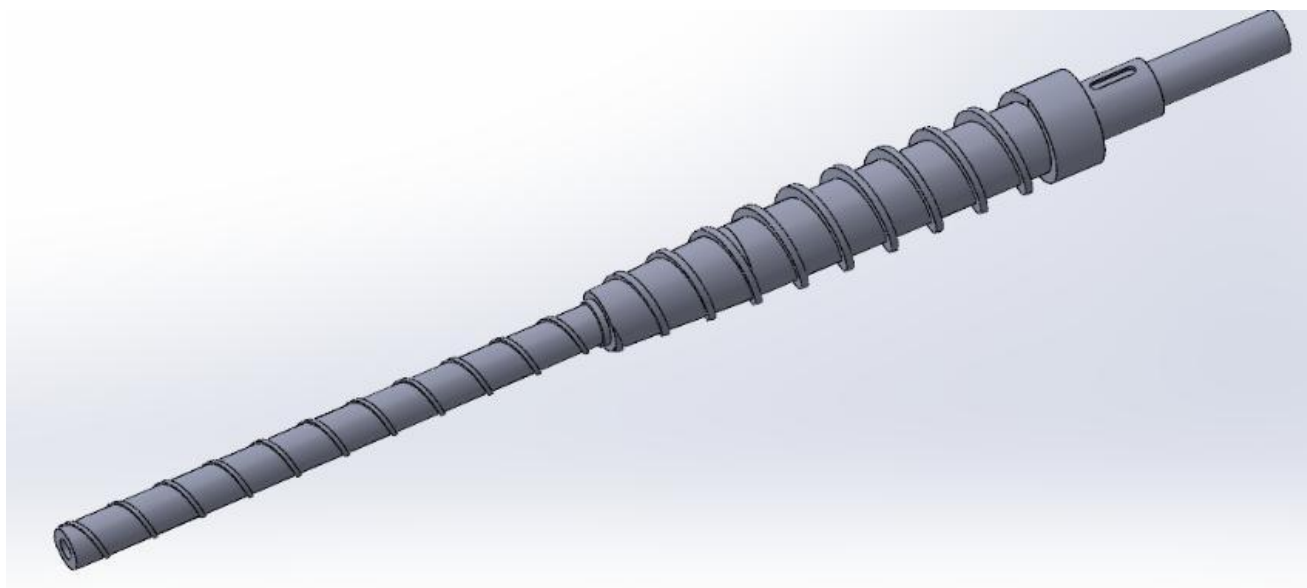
3D-модель модернізованого двосекційного черв'яка (SolidWorks)
